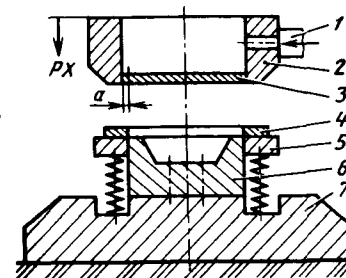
Схема вырубки плоской заготовки на вырубном штампе с верхним расположением матрицы: 1 — подача воздуха для выталкивания заготовки; 2 — матрица; 3 — плоская заготовка; 4 — полоса; 5 — съемник; 6 — пуансон; 7 — подушка
